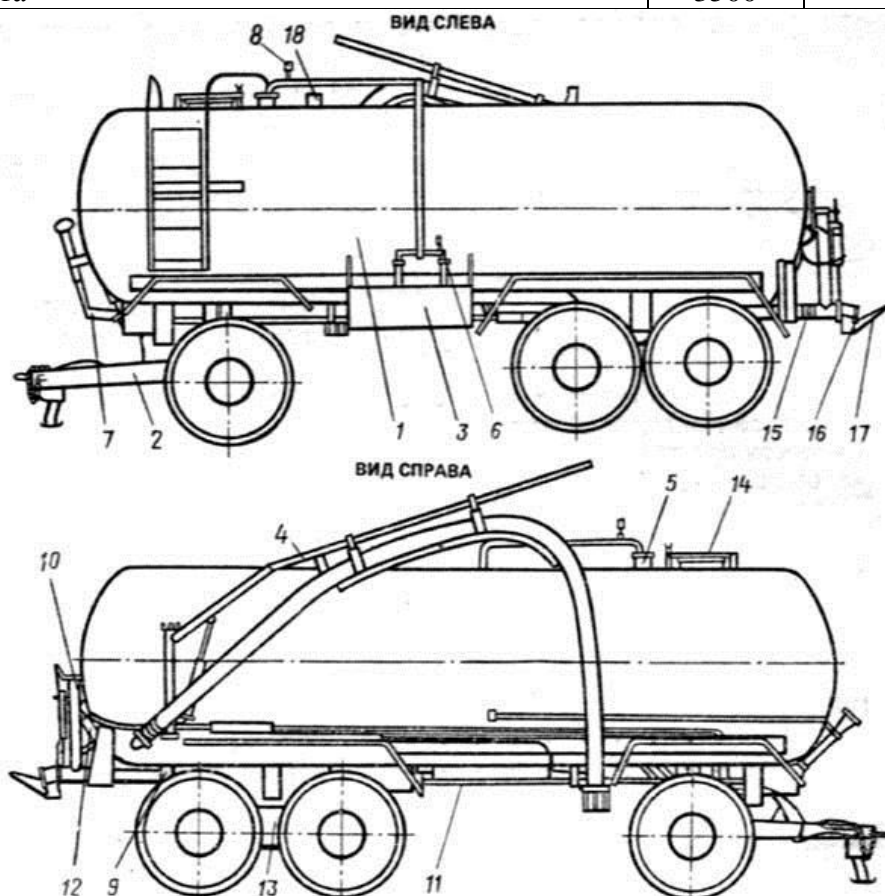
Машина МЖТ-16: 1 – цистерна; 2 – тележка; 3 – вакуумная установка; 4 – заправочная штанга; 5 – предохранительный клапан жидкостный; 6 – предохранительный клапан вакуумный; 7 – уровнемер; 8 – вакуумметр; 9 – центробежный насос; 10 – переключающее устройство; 11 – силовая передача; 12 – люк; 13 – балансирная подвеска; 14 – люк; 15 – напорный трубопровод; 16 – разливочное устройство; 17 – заслонка; 18 – предохранительный клапан.
